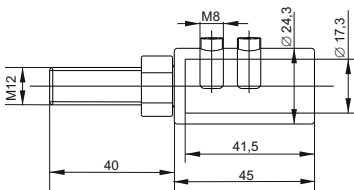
Габаритные размеры соединителя / Figure 1 – Overall dimensions of the connector /
